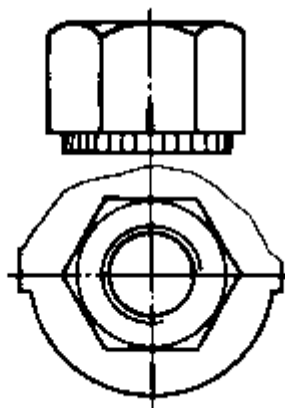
Схема нанесения рисок на крышке цилиндров
